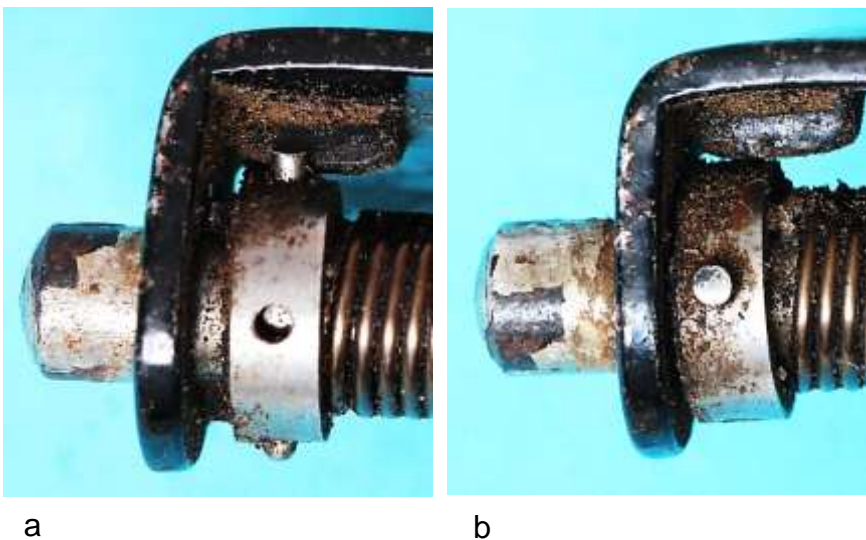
Drehwinkelzapfen am Umfang der Arretierscheibe: a) Betriebsstellung, b) Ruhestellung
